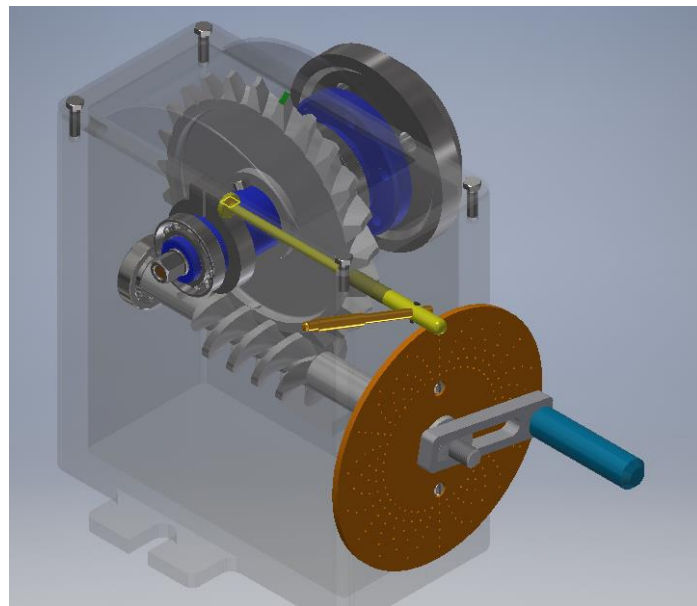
Зовнішній вигляд ділильної головки з прозорим корпусом
